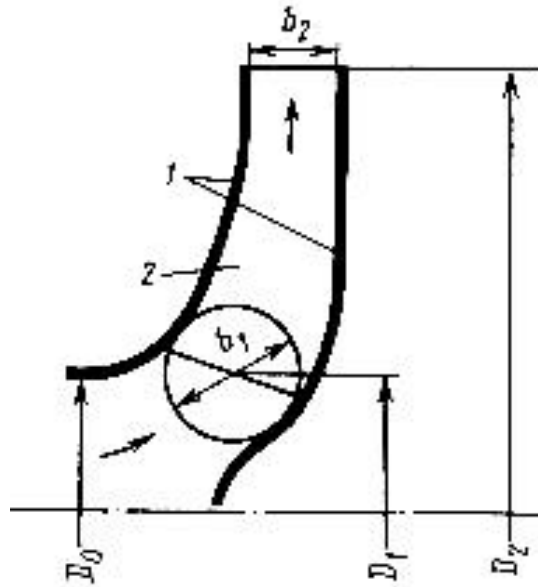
Меридіанний перетин проточної частини робочого колеса лощиною, що проходить через вісь його обертання: 1 – диски; 2 – робоча лопать.
